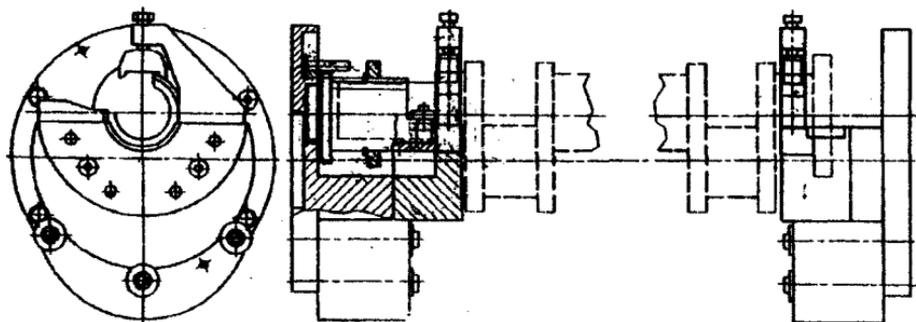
Устройство для шлифовки шатунных шеек коленчатых валов ДВС
